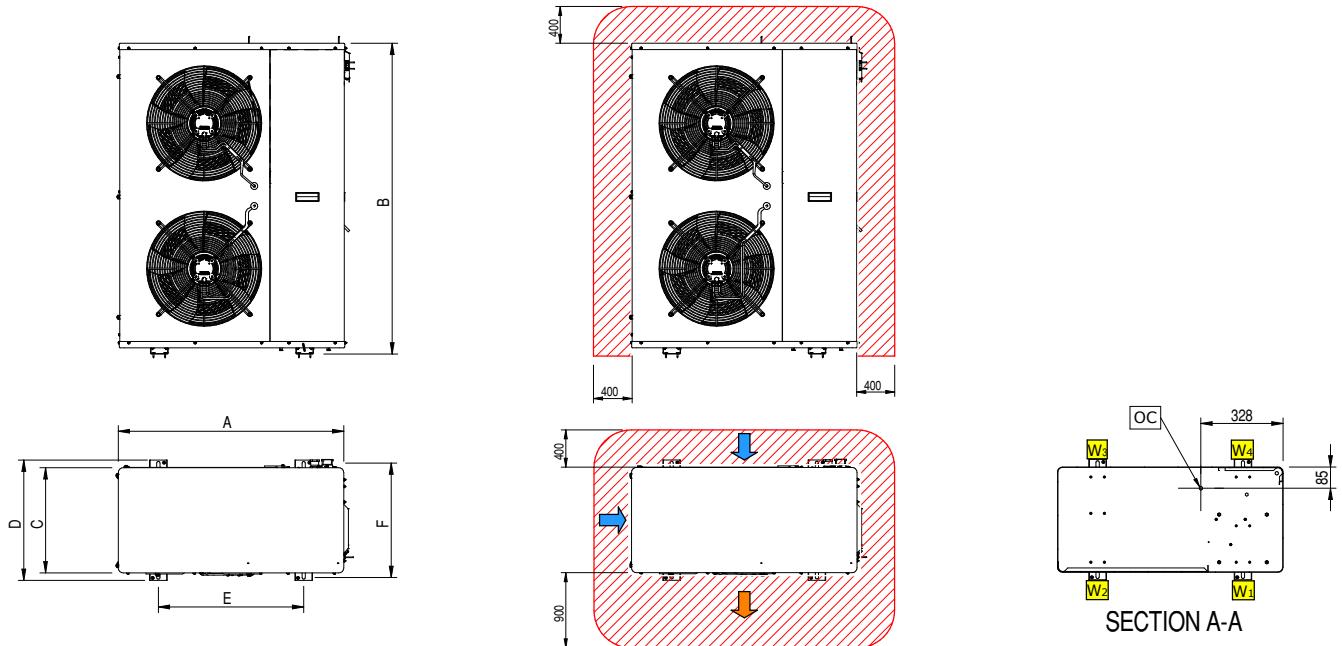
disegno dimensionale taglie 11V, 15V e 15Y
